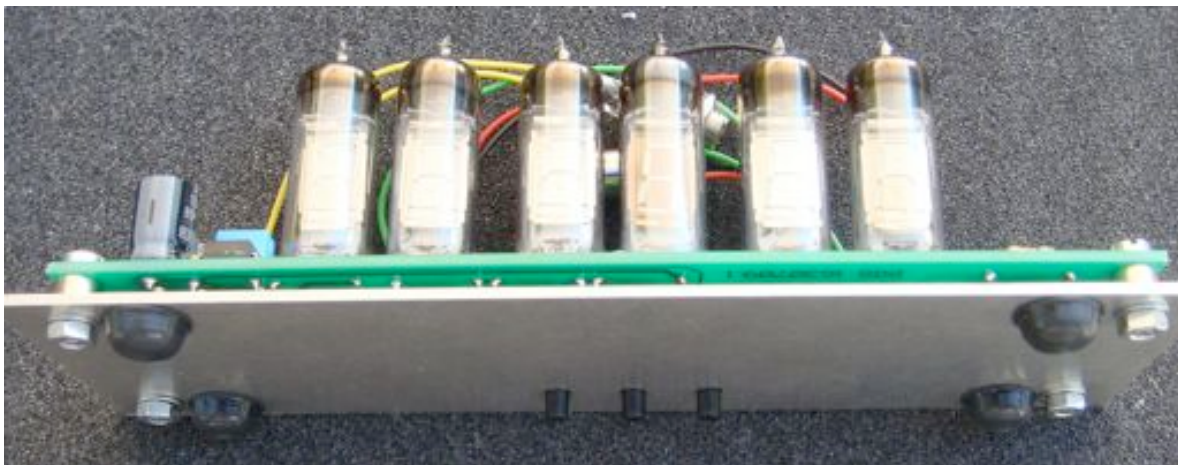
Montage der Bodenplatte – Taster in gefrästen Löchern
